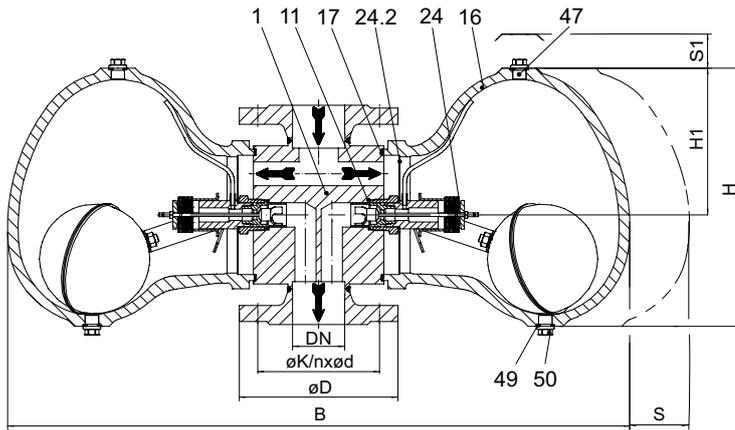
1 mit Flanschen - vertikale Einbaulage
